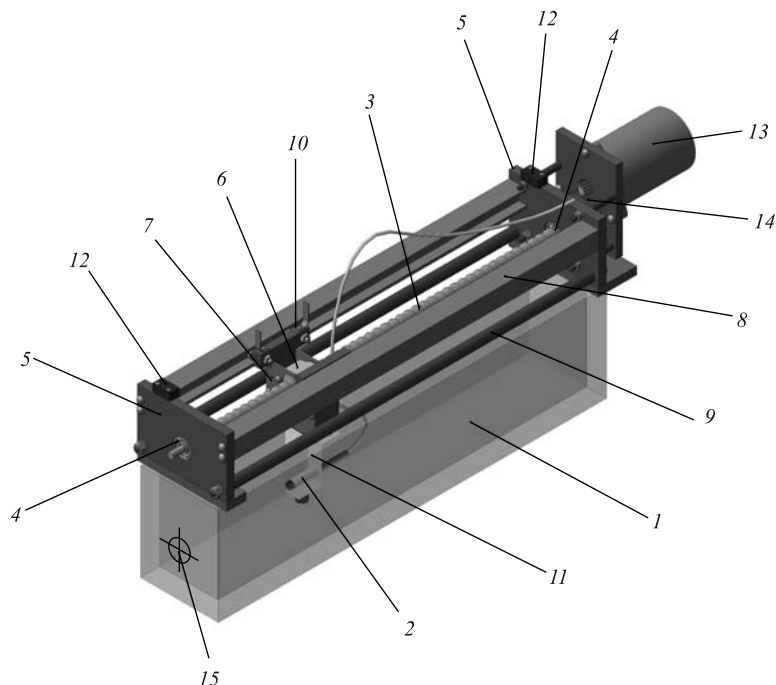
Общий вид анализатора для измерения глубинно-дозовых распределений медицинского протонного пучка («мини-дозографа»): 1 — ванна; 2 — детектор; 3 — «червяк»; 4 — подшипники; 5 — боковины; 6 — гайка; 7 — каретка; 8 — направляющие рельсы; 9 — горизонтальные шпильки; 10 — подшипники каретки; 11 — держатель детектора; 12 — концевые выключатели; 13 — шаговый двигатель; 14 — редуктор; 15 — метка «прицел»
